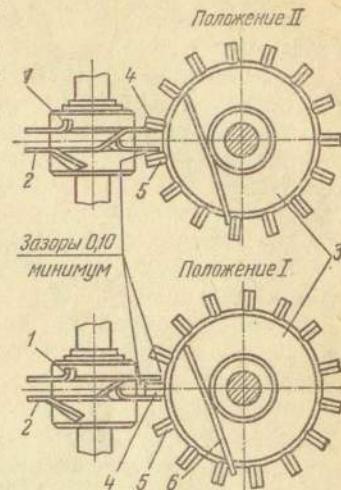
Палетно-червячный преобразователь (взаимное расположение зубьев анкерного колеса и палетных дисков):
